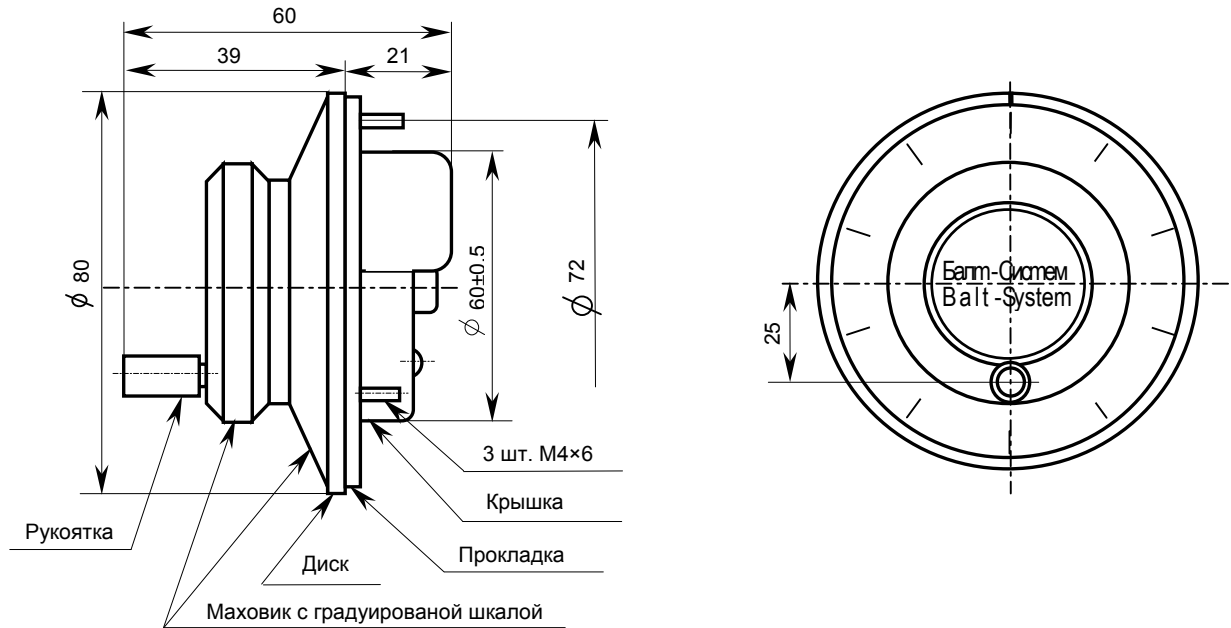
Габаритные размеры штурвала LGF-12-003B-100
